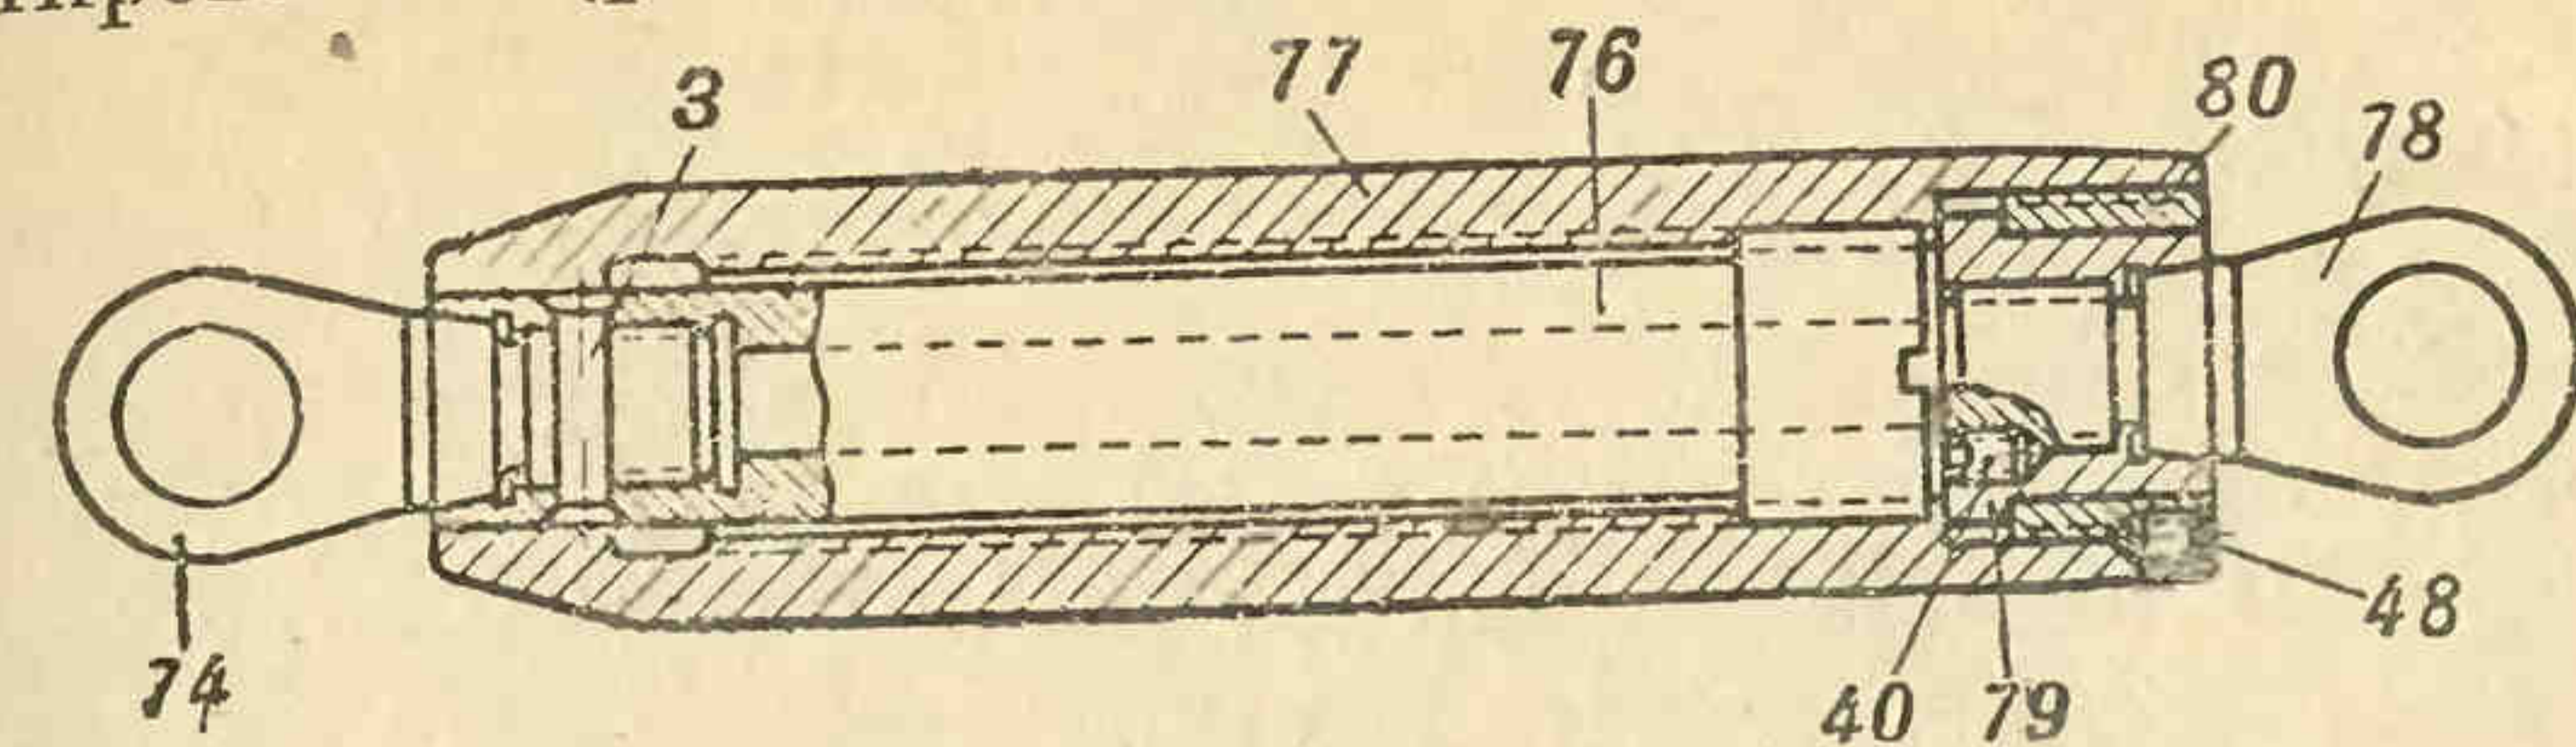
Механизм точного горизонтирования: 74 — ушко (проушина) (2-43); 76 — винт (2-45); 77 — корпус (2-46); 78 — ушко; 79 — втулка; 80 — втулка; 3 — заклепка (2-47).
